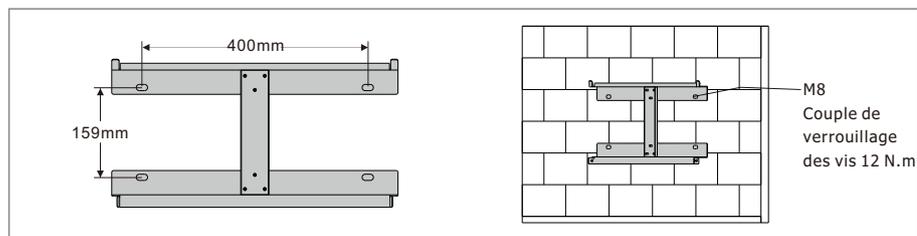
Installer la plaque de suspension de l'onduleur
